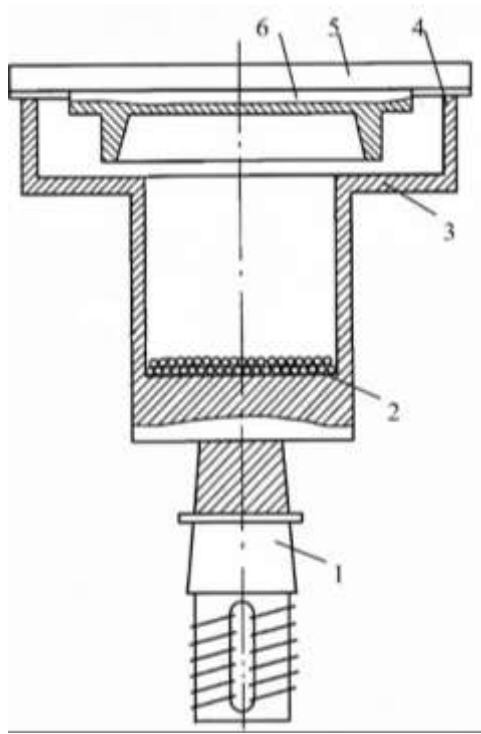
Ультразвуковий пристрій для зміцнення деталей:
